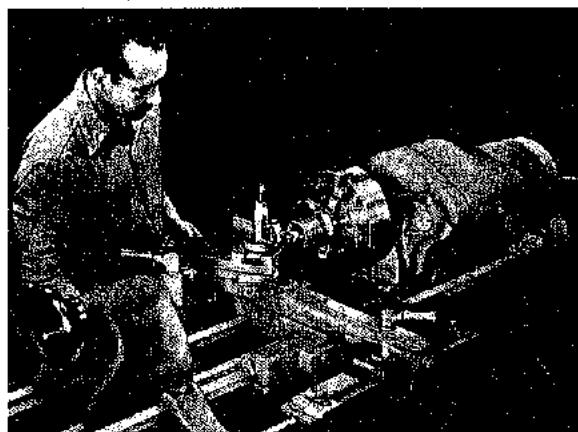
Tallado de una rosca en el torno (South Bend Lathe Works).
